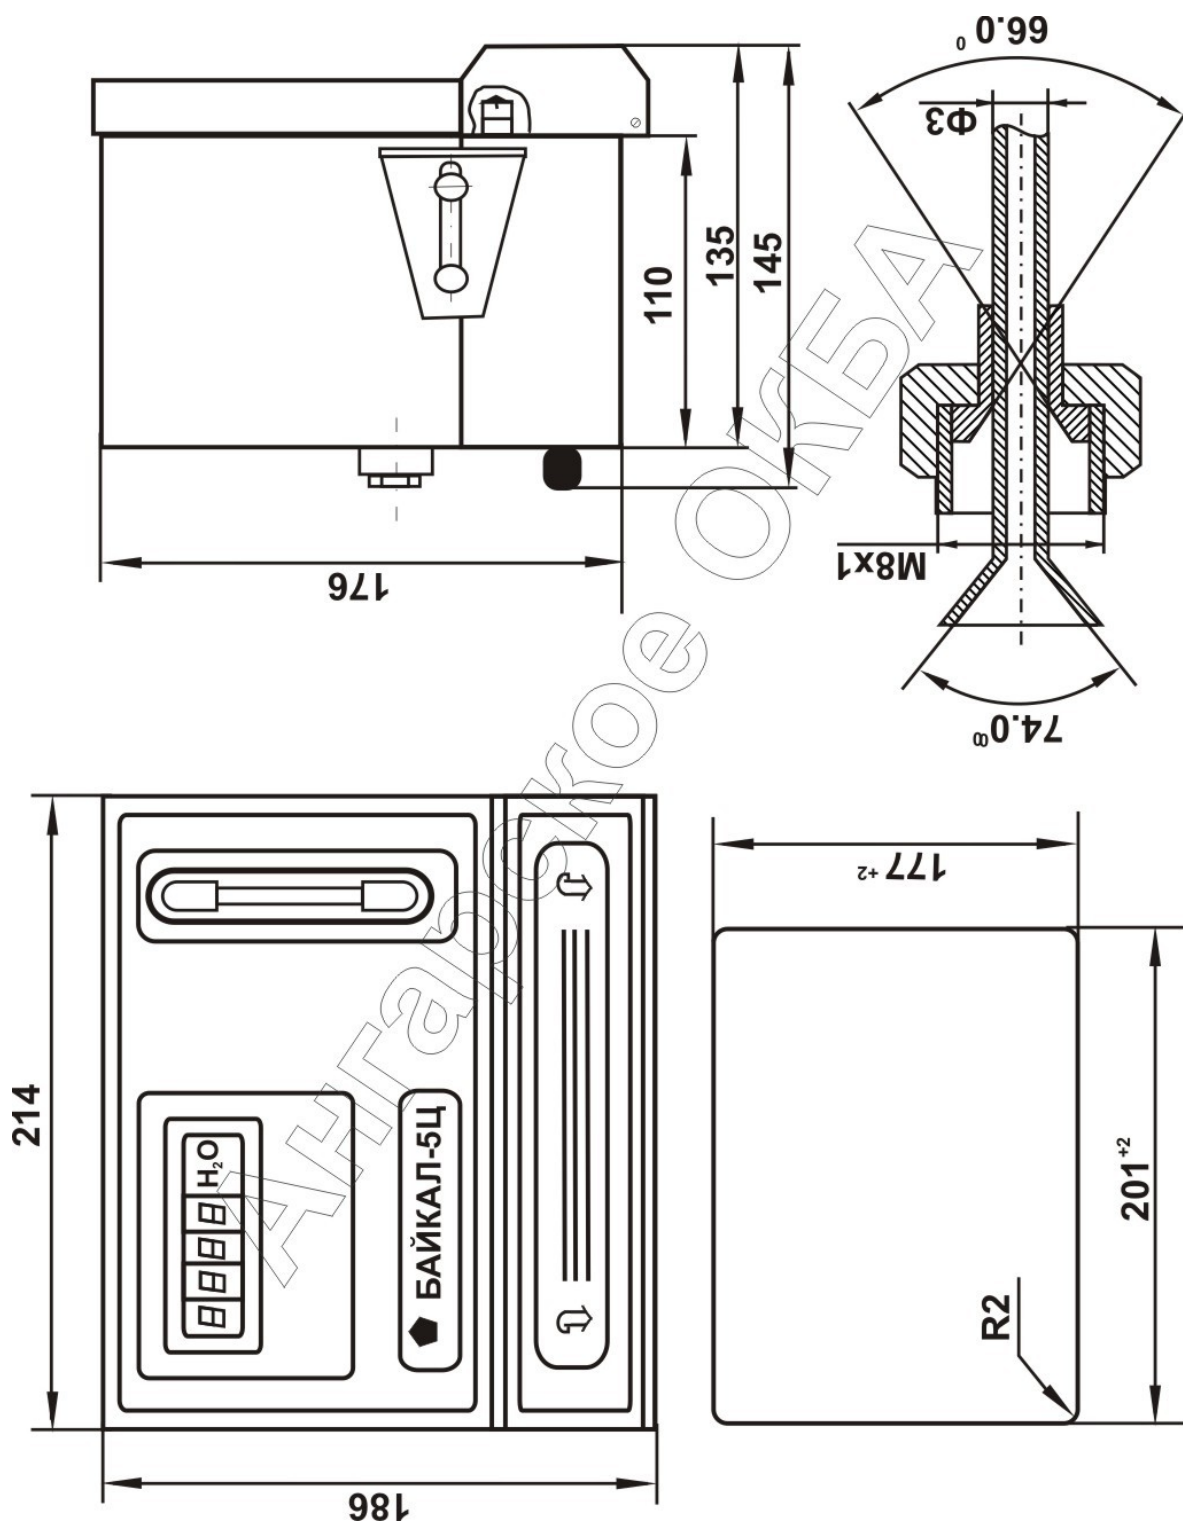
Гигрометр БАЙКАЛ-5Ц. Габаритно-установочный чертёж.
